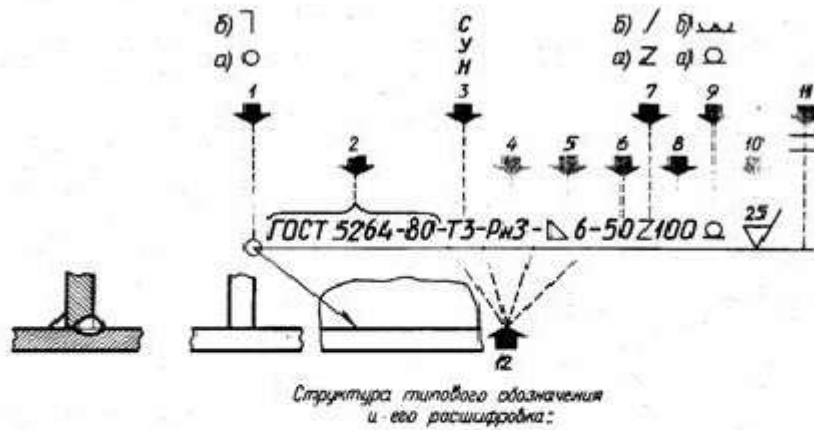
Структура обозначения шва сварного соединения (сварка плавлением):
